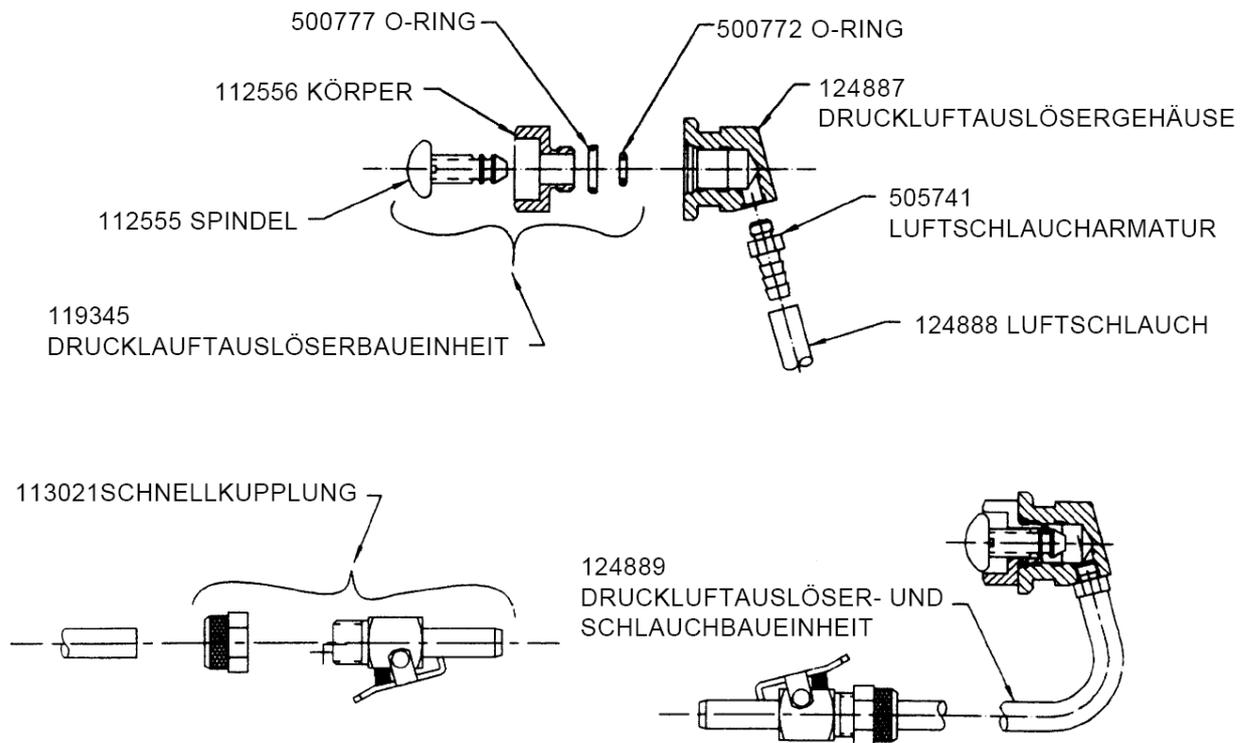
Explosionsansicht und zusammengebaute Bauteile
